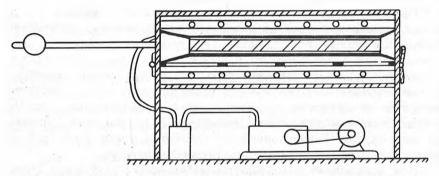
Схема вакуумного процесса для двустороннего облицовывания заготовок:
